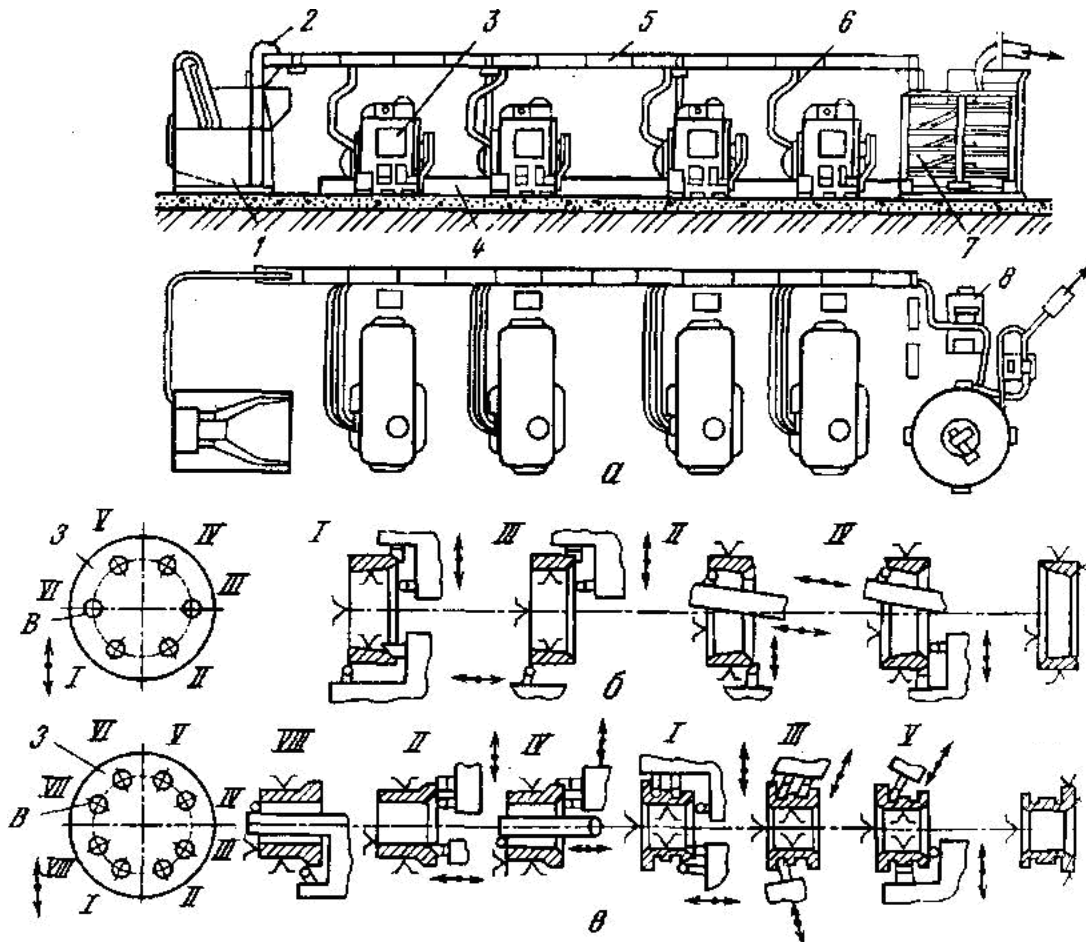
Автоматична лінія токарної обробки кілець конічних роликів підшипників: а – загальний вигляд; б – обробка зовнішніх кілець; в – обробка внутрішніх кілець; "З" – завантаження; "В" – вивантаження
